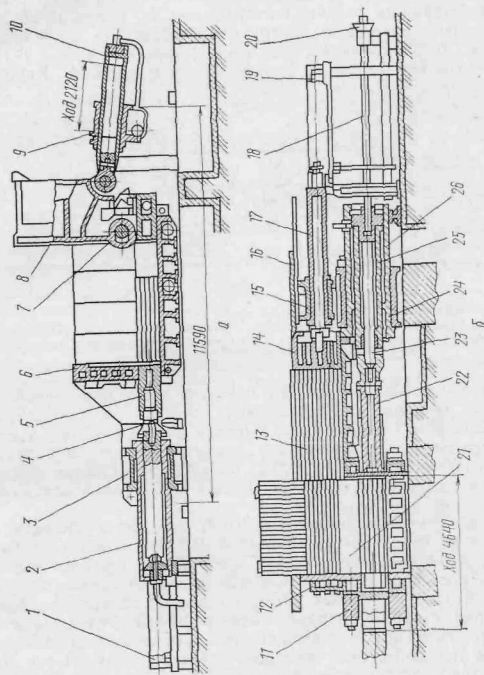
Поперечный (а) и продольный (б) разрезы пакетировочного пресса В-101
